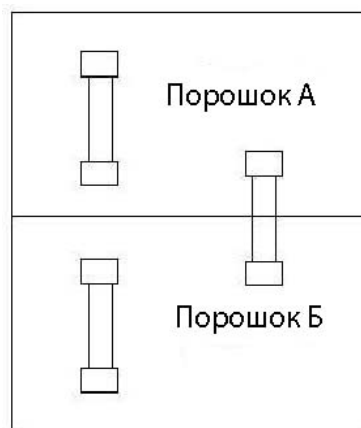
Схема вырезки образцов из горячепрессованного блока
